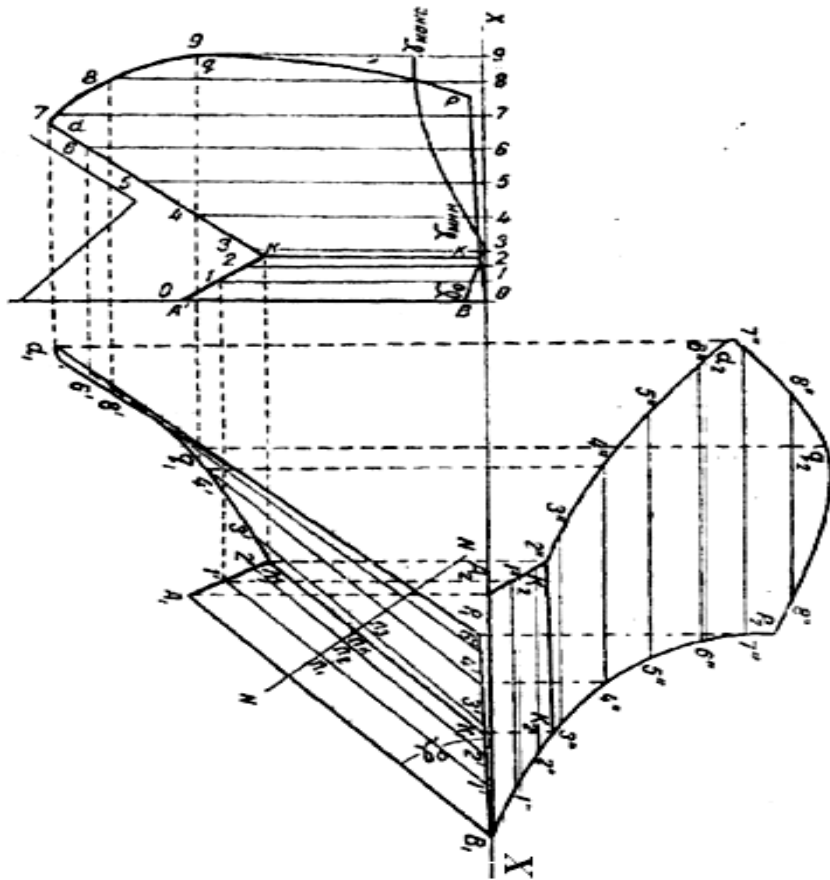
Построение горизонтальной и профильной проекции рабочей поверхности корпуса
